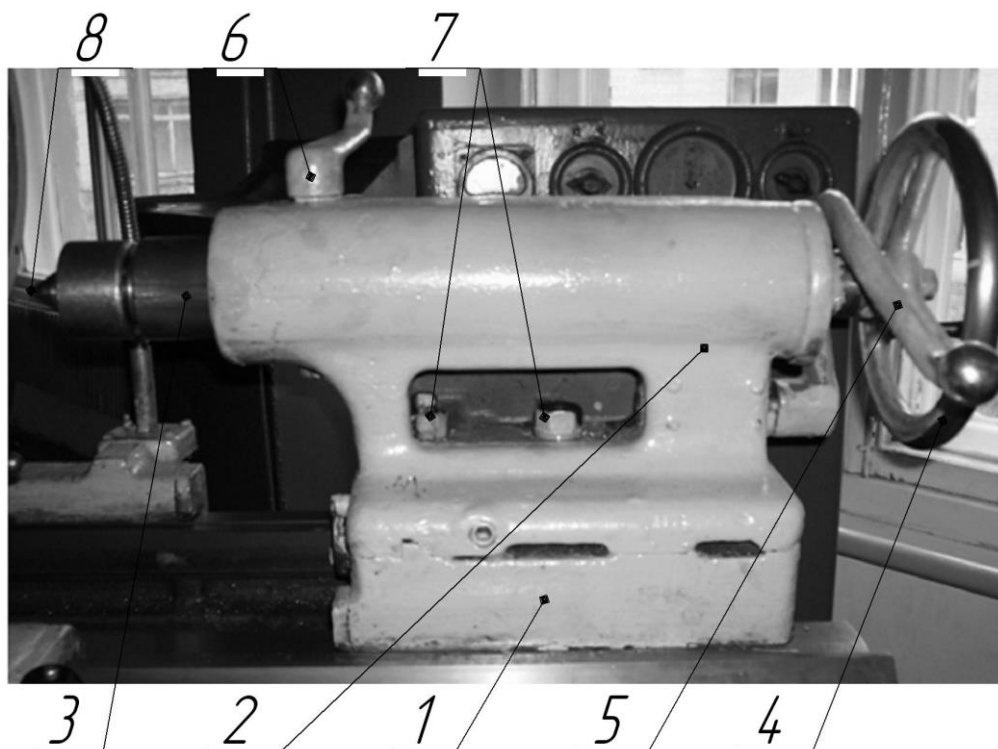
Задняя бабка: 1 – плита, 2 – корпус, 3 – пиноль, 4 – маховик, 5 – рукоятка, фиксирующая положение бабки на станине, 6 – рукоятка, фиксирующая положение пиноли, 7 – болты крепления, 8 – центр
